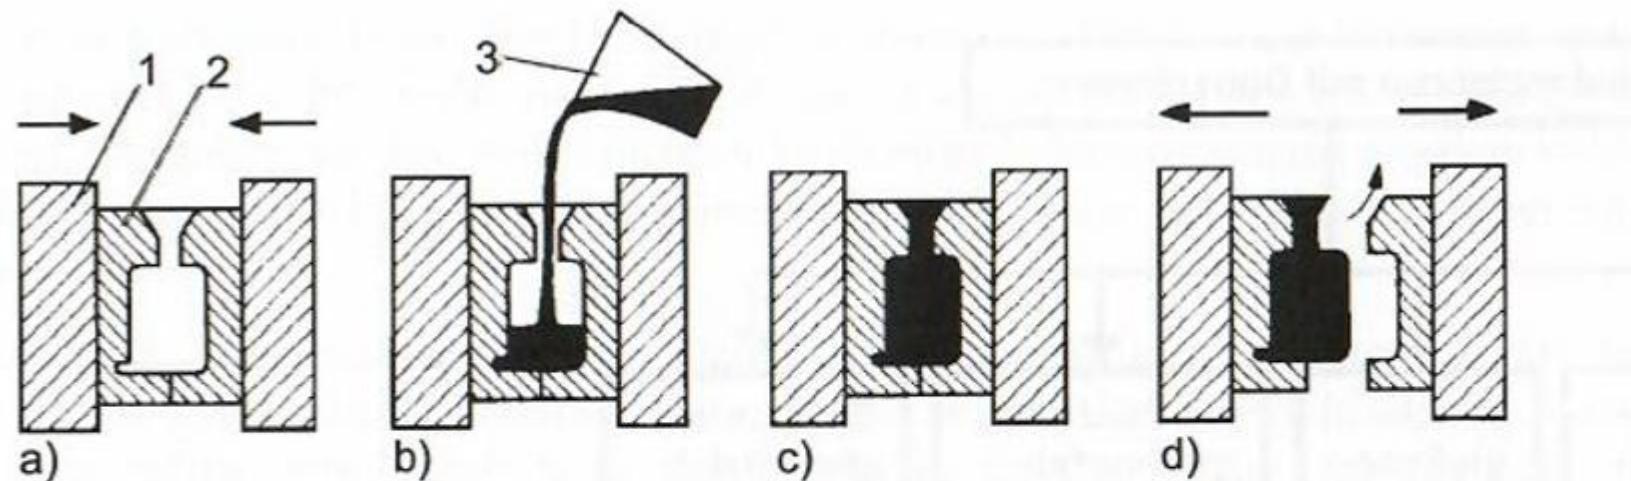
Verfahrensablauf des Schwerkraftkokillengießverfahrens
